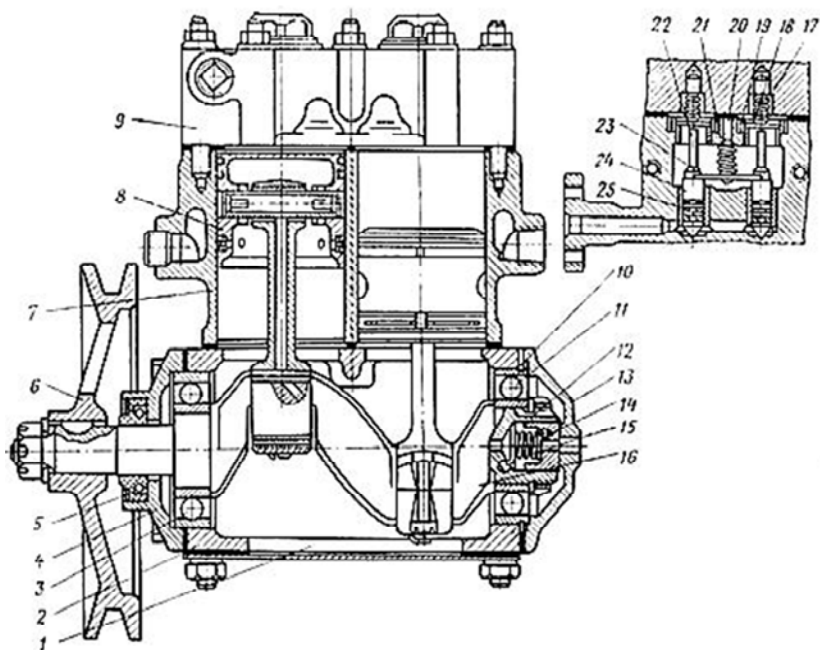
Двухцилиндровый компрессор автомобиля МАЗ:
